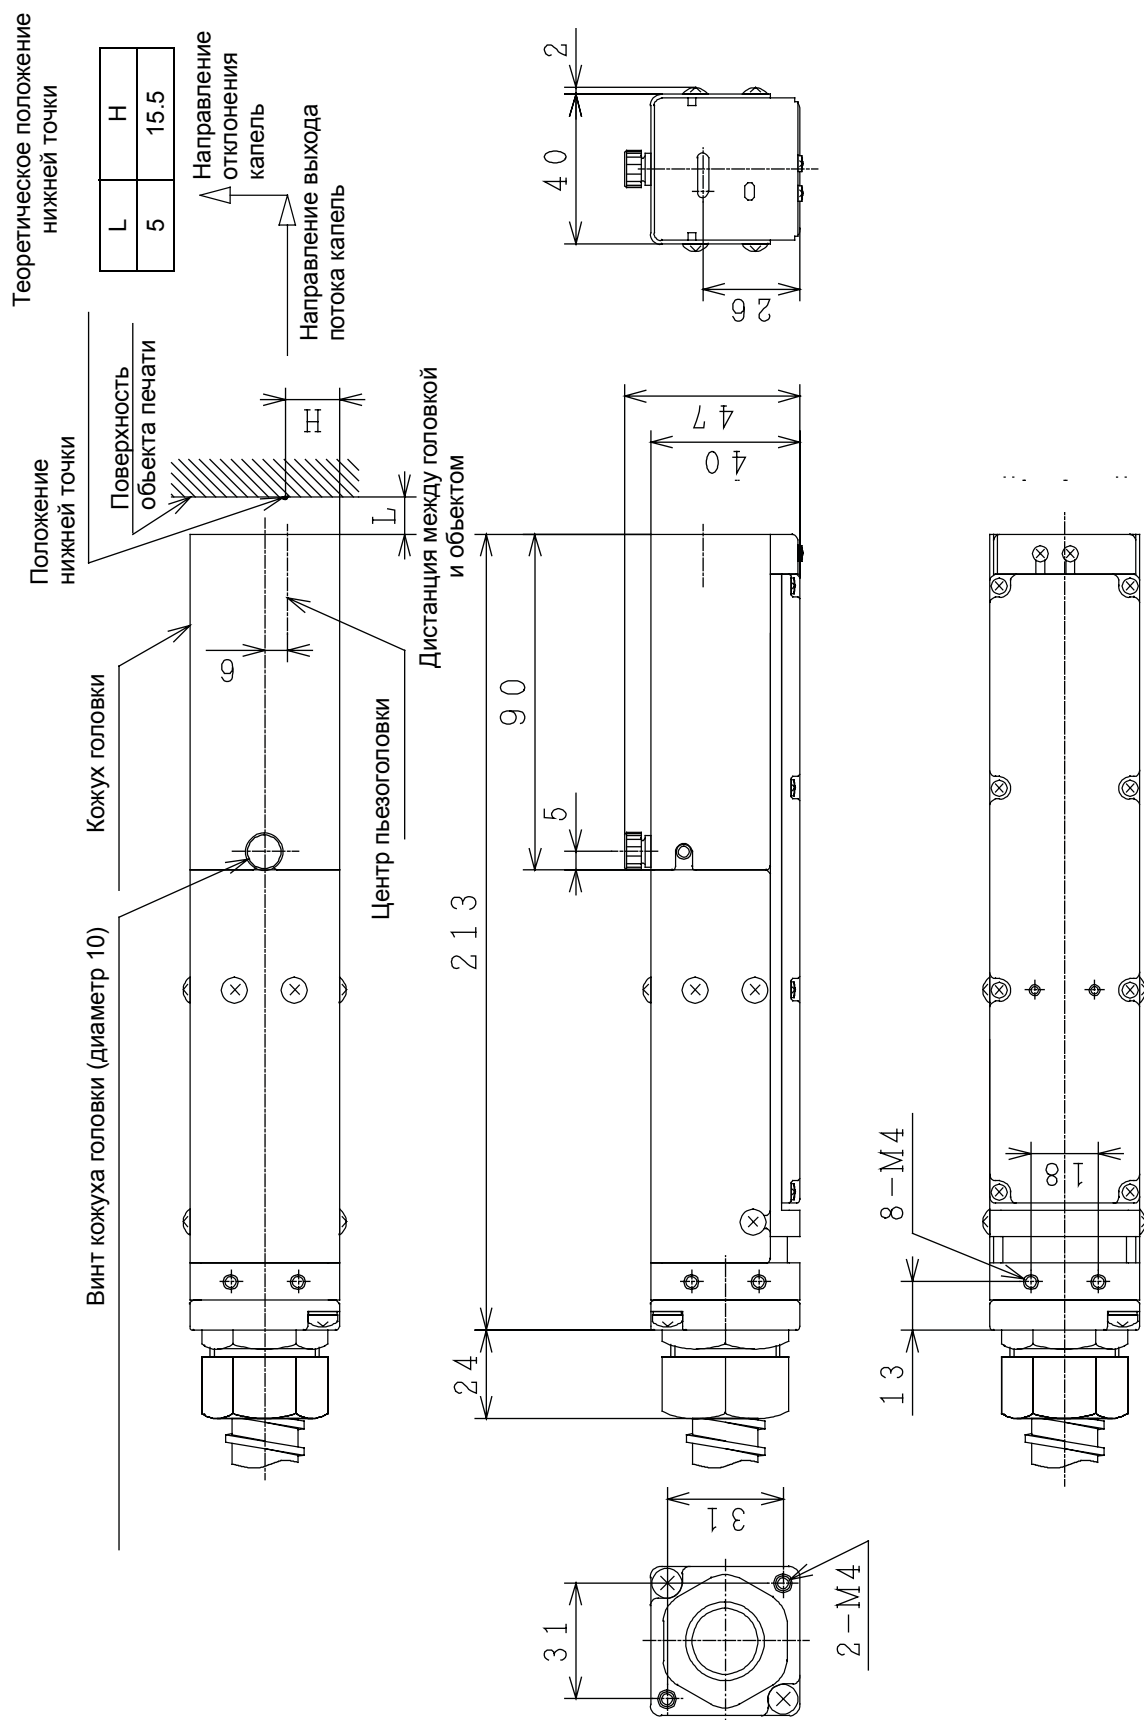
Размеры печатающей головки (сопло 40 μm)
